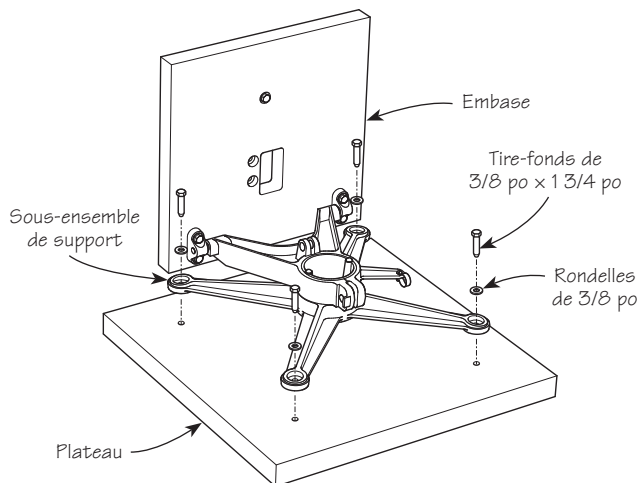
Assemblage du sous-ensemble de support au plateau. L'embase est relevée pour montrer l'assemblage.
